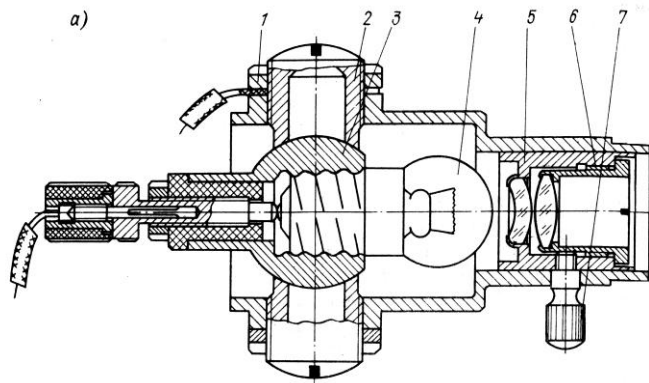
Приладовий освітлювач: 1 – корпус; 2 – дві різьбові опори; 3 – сферичний шарнір; 4 – лампа; 5 – оправа; 6 – втулка; 7 – поводок
